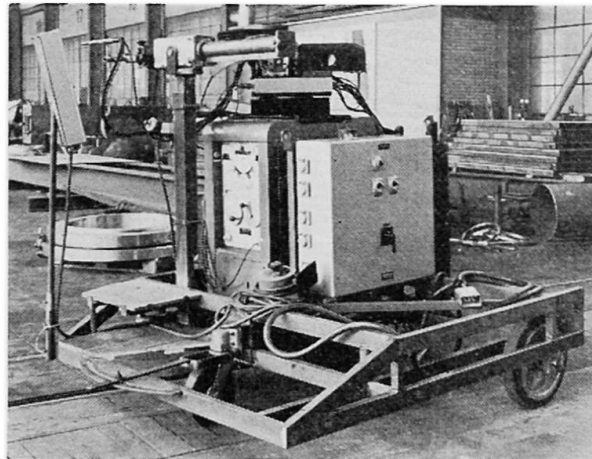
Prototyp der CO₂-Schutzgas-Schweißapparat.
